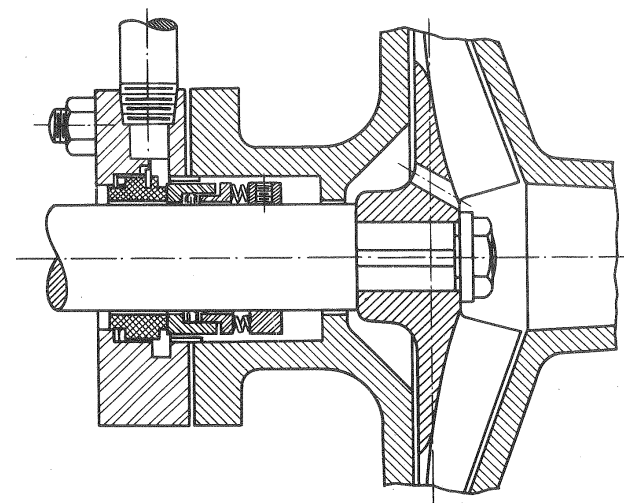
Cierre mecánico para una B química Lawrence.
